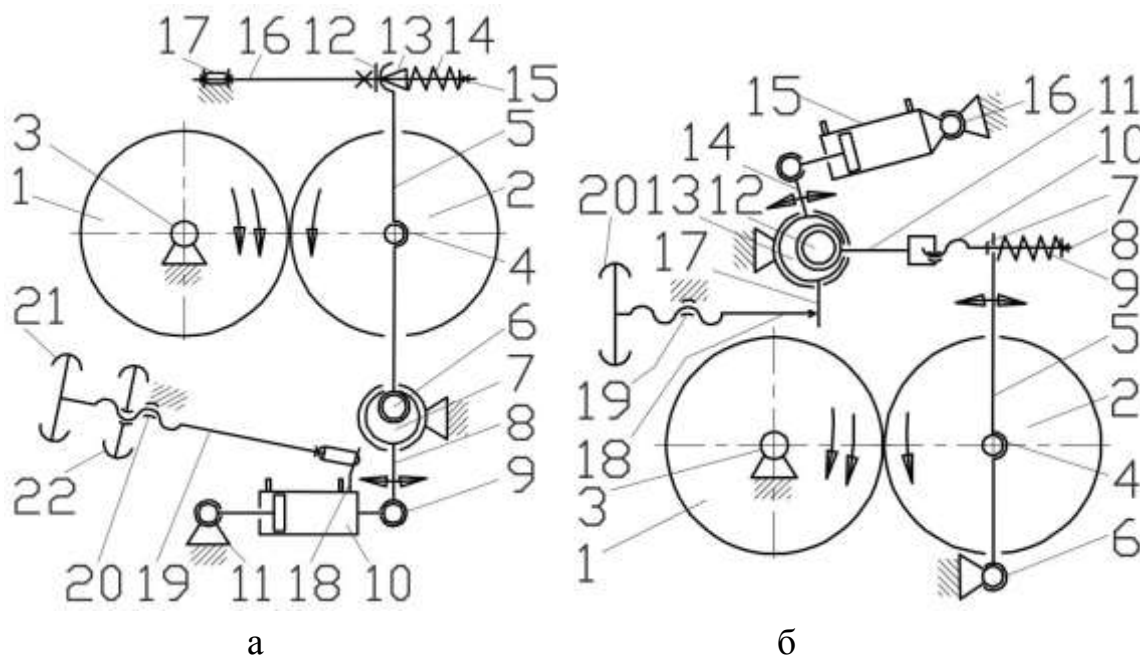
Схеми установчих механізмів вальцьових верстатів.
